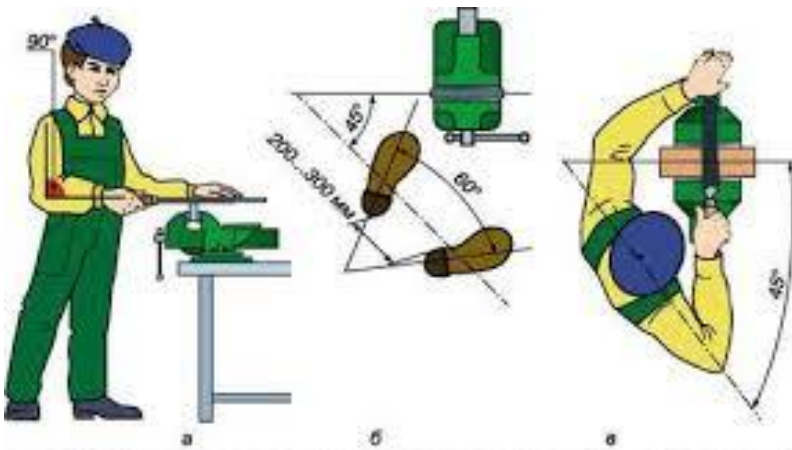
Робоча поза: *a* – положення тулуба;
